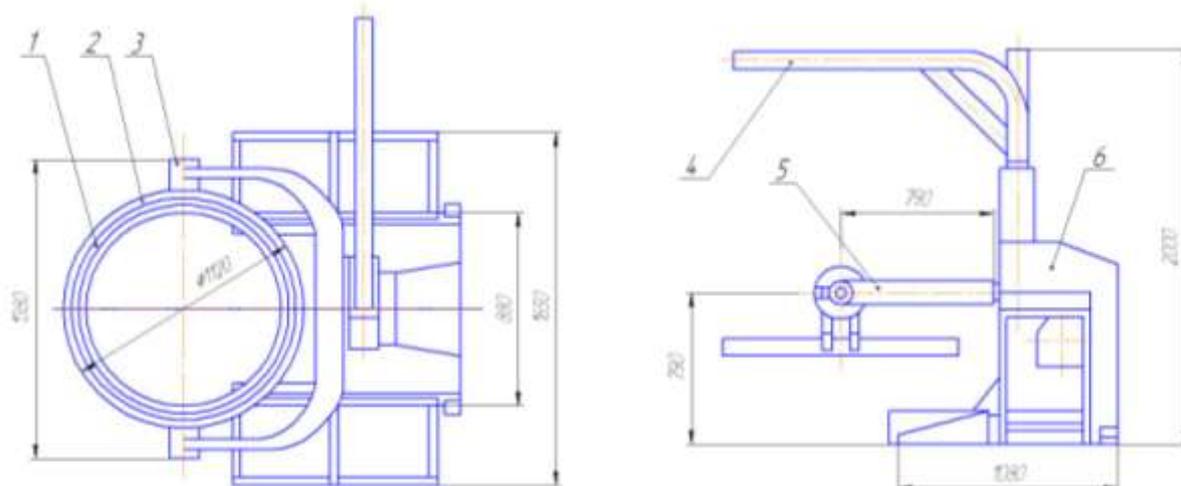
Стенд для разборки и сборки V- образных двигателей (Модель 6501-72)
